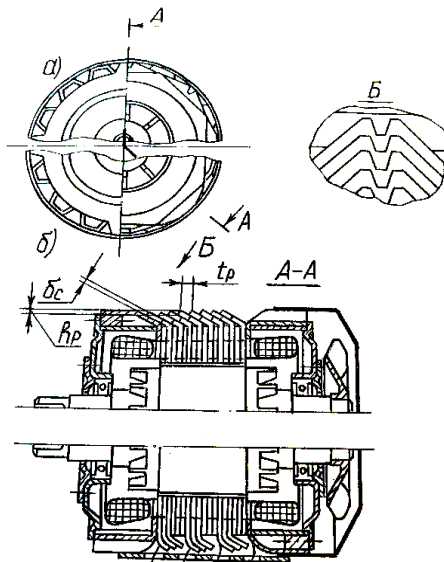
Закритий безкорпусний двигун, що обдувається, з багатоплощинним магнітопроводом статора і штампованими конструкційними елементами:
